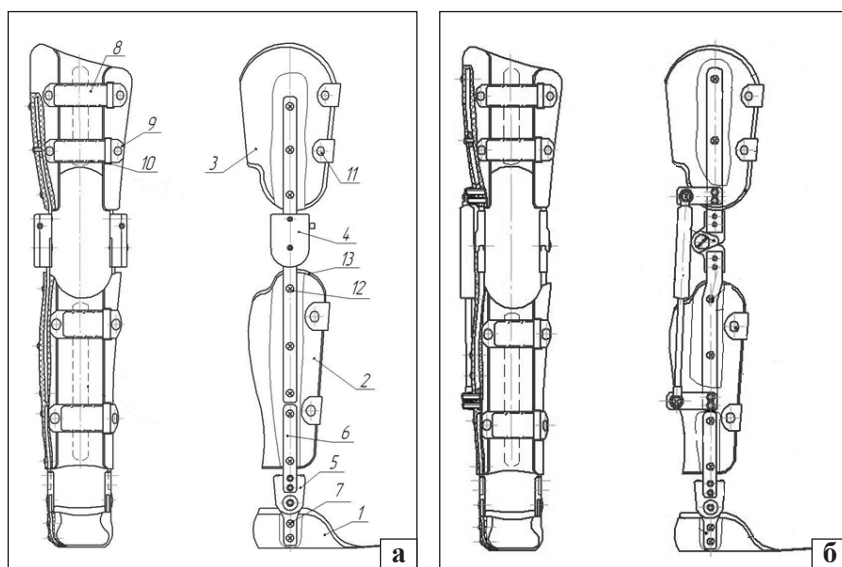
Конструкции динамических ортезов на коленный и голеностопный суставы (стопу): а) с коленными шарнирами, регулирующими плоскими спиральными пружинами; б) с пневмоцилиндром
